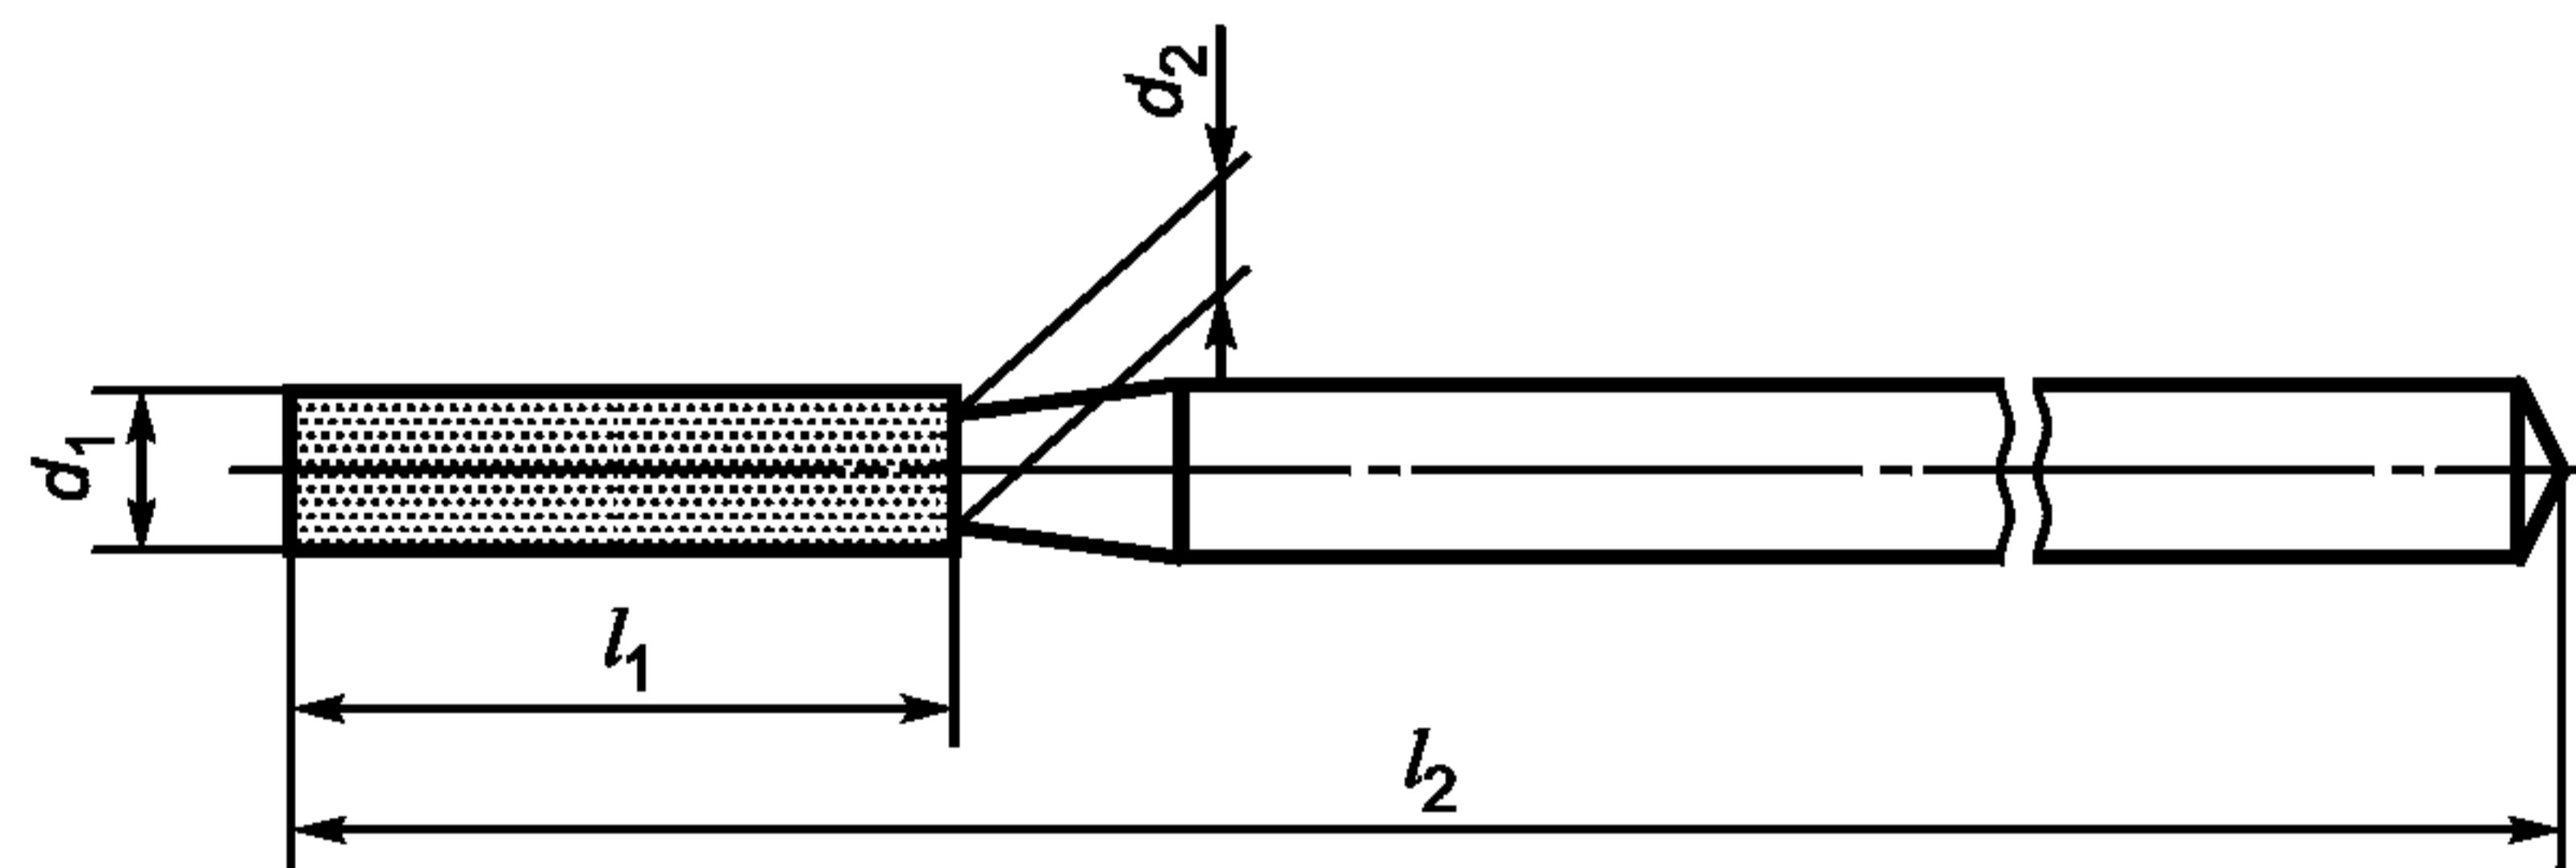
Цилиндрическая рабочая часть с длиной головки 10,0 мм
